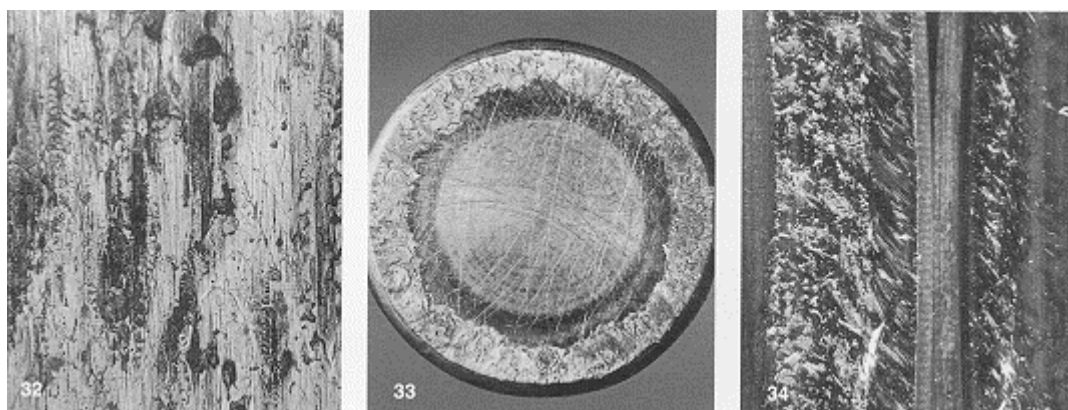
Задиры на торцевой поверхности ролика сферического роликоподшипника; 100-кратное увеличение
